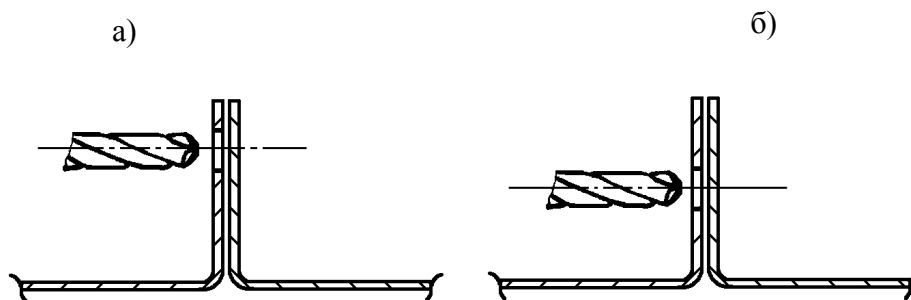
Расположение сварочных точек на кромках детали
